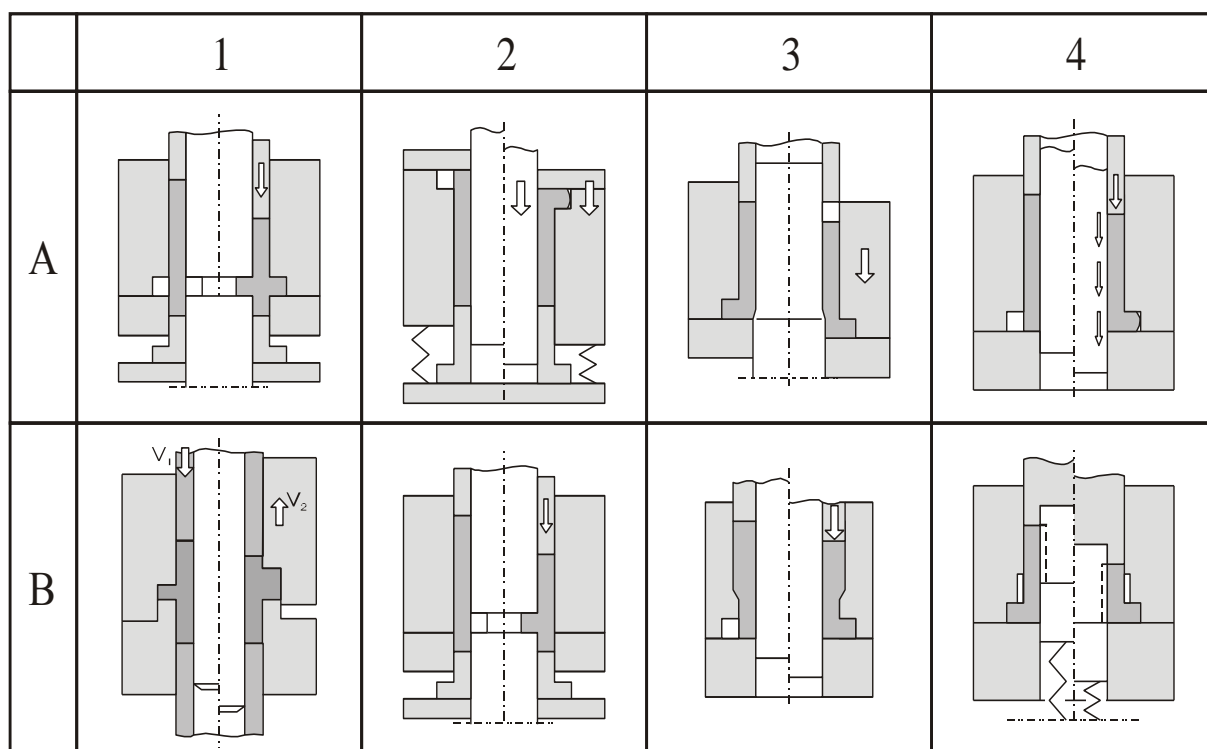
Способи видавлювання деталей типу втулок з фланцям
